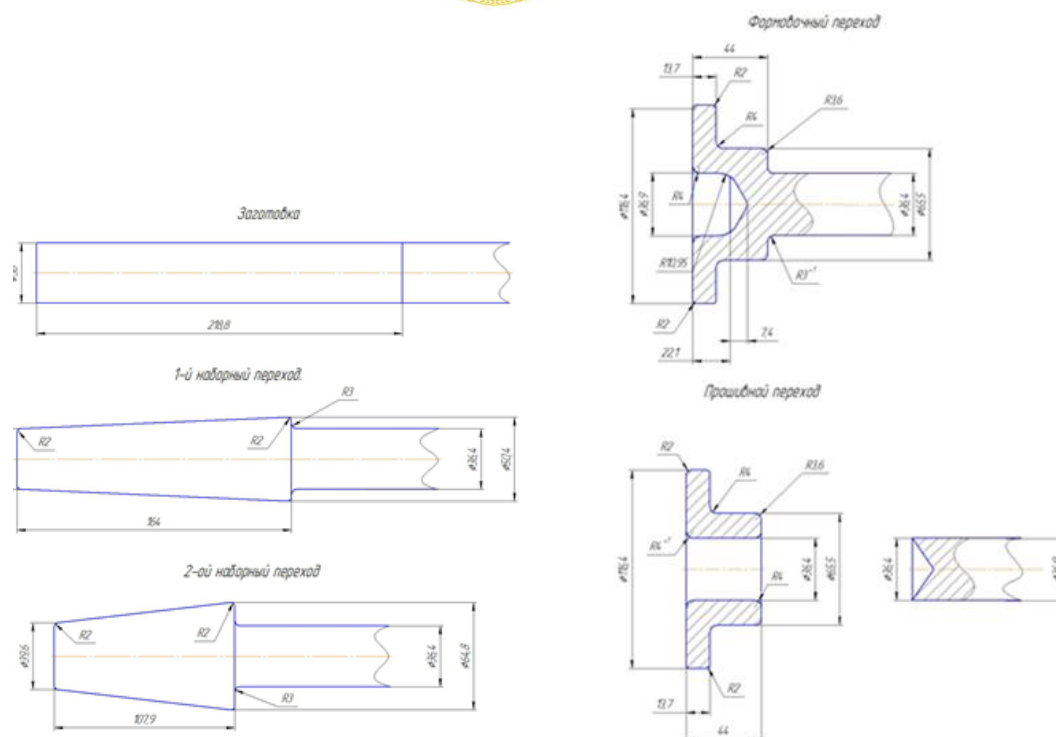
Переходы штамповки поковки типа втулки с фланцем на ГКМ
